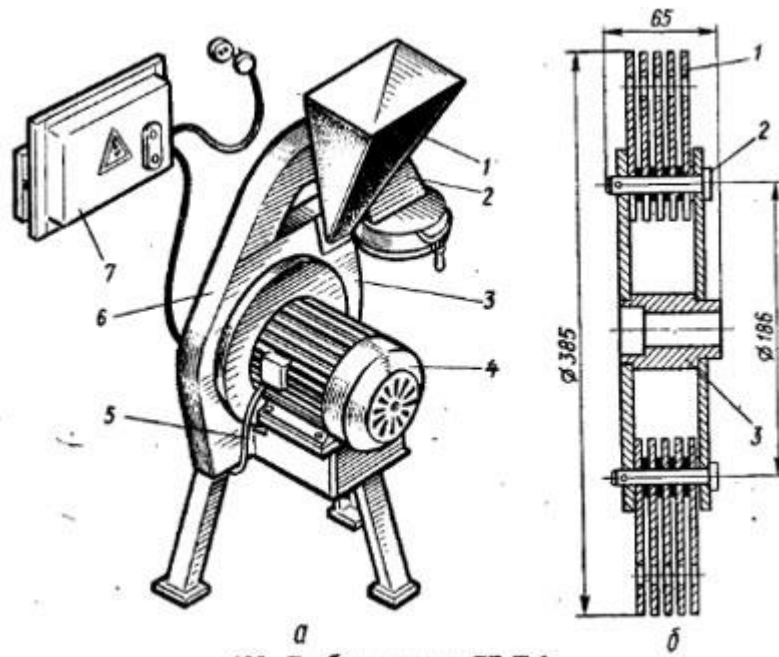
Дробарка зерна ДЗ-Т-1: а- загальний вигляд, 1 – загрузочний бункер, 2 – патрубок вивантаження, 3 – корпус, 4 – електродвигун, 5 – провід, 6 – направляючий канал, 7 – блок конденсатора; б – молотковий ротор; 1 – молоток; 2 – палець; 3 – ротор;
